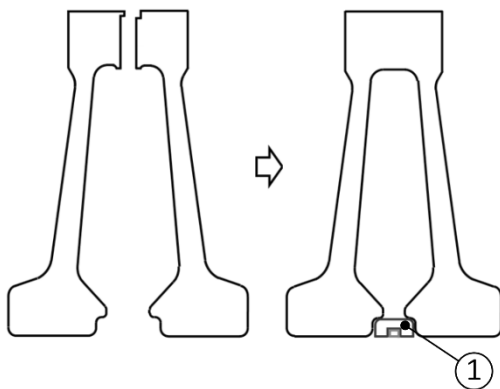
Общий вид пустотелой разрезной сварной конструкции диска
